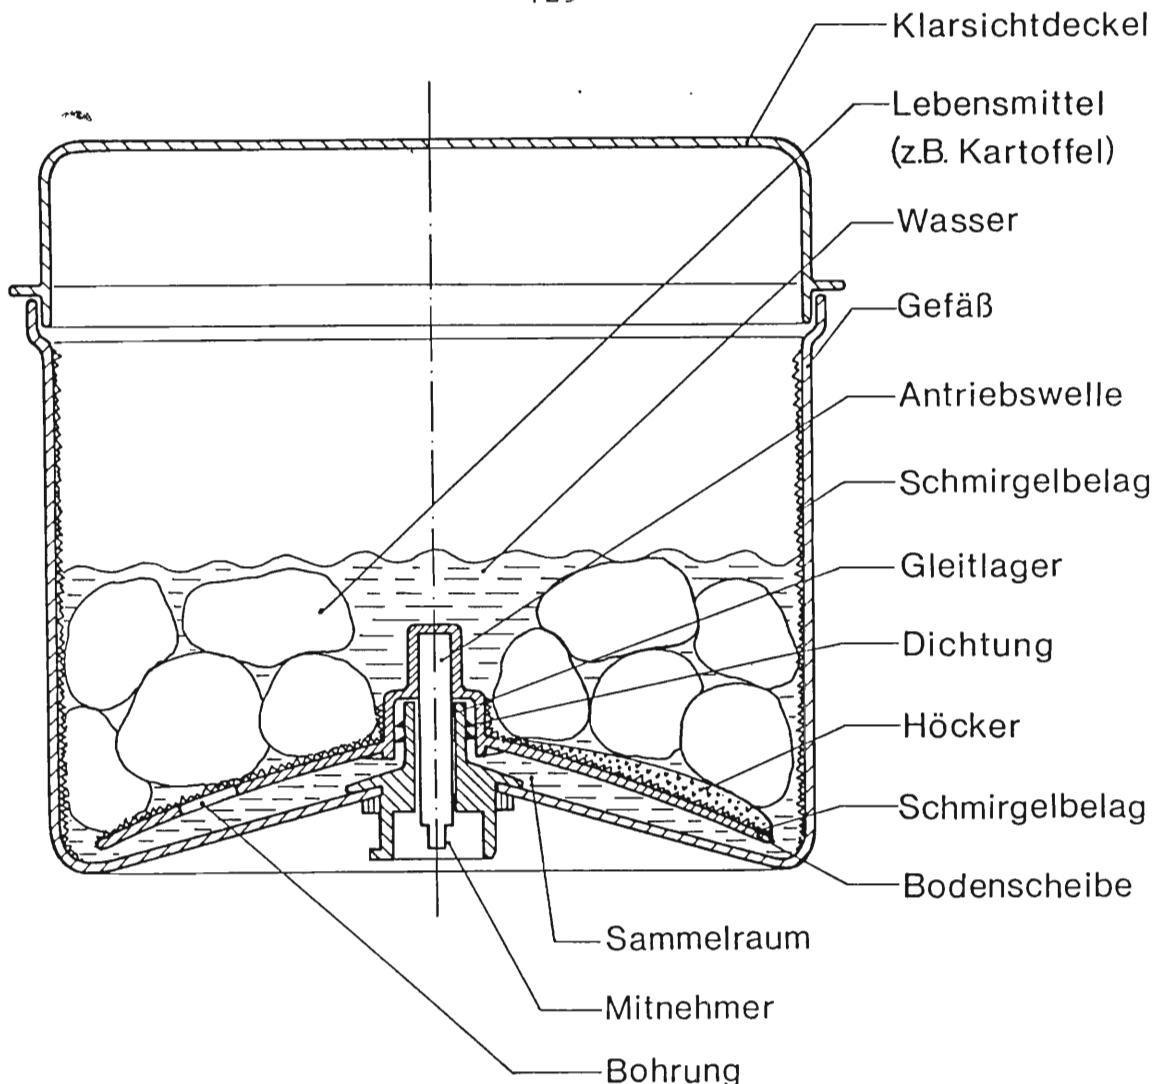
/9: Schälgerät mit korundbeschichteten Wirkflächen für Fremdantrieb (Stand-Küchenmaschine)
